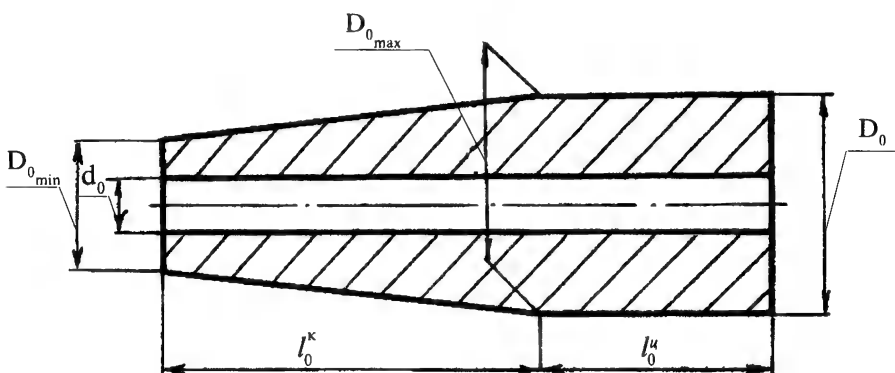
Схема к расчету размеров цилиндро-конической заготовки
